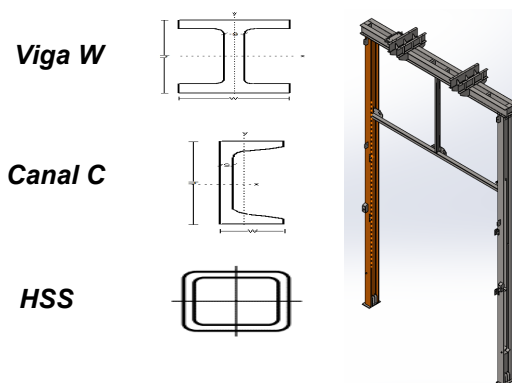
Perfiles propuestos y partes principales de la estructura del sistema de levante a analizar.
